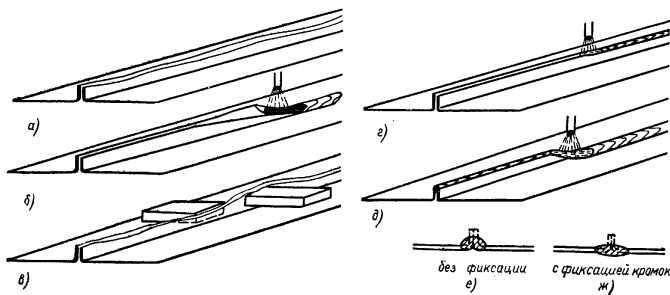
Схемы сварки с фиксацией отбортованного соединения
